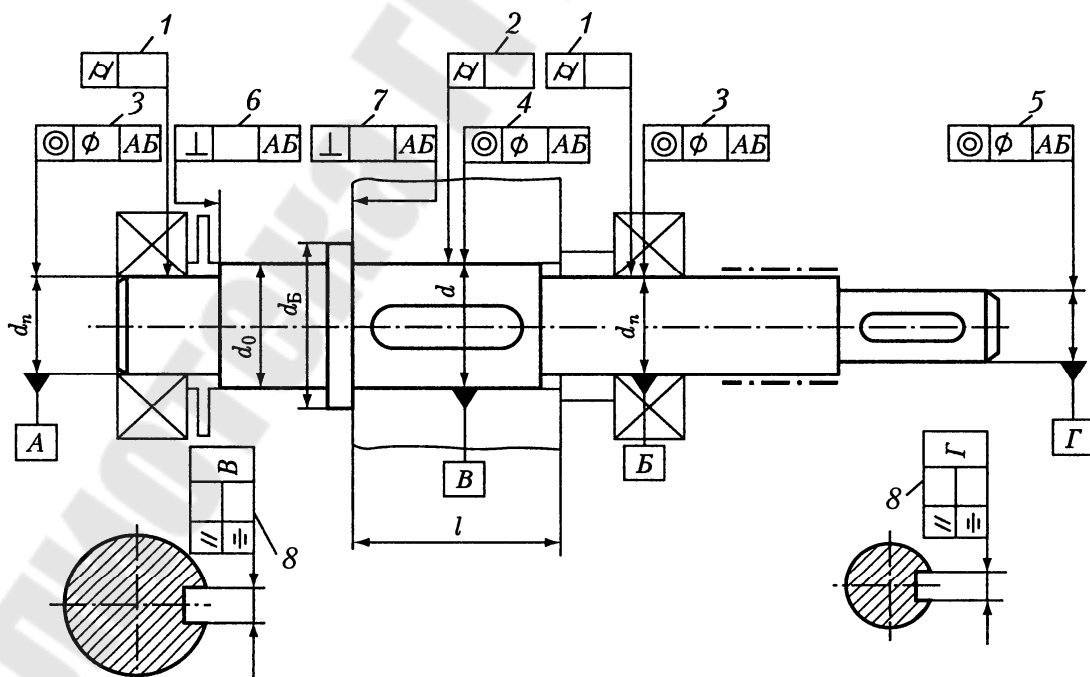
Указание на чертеже вала допусков формы и расположения
